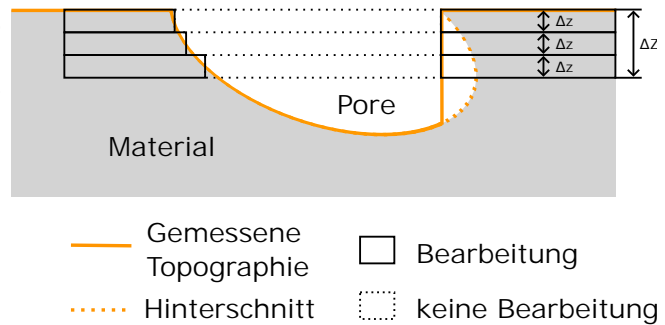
Bearbeitungsmasken im Querschnitt mit Diskretisierungsfehler (links) und Hinterschnitt (rechts).
